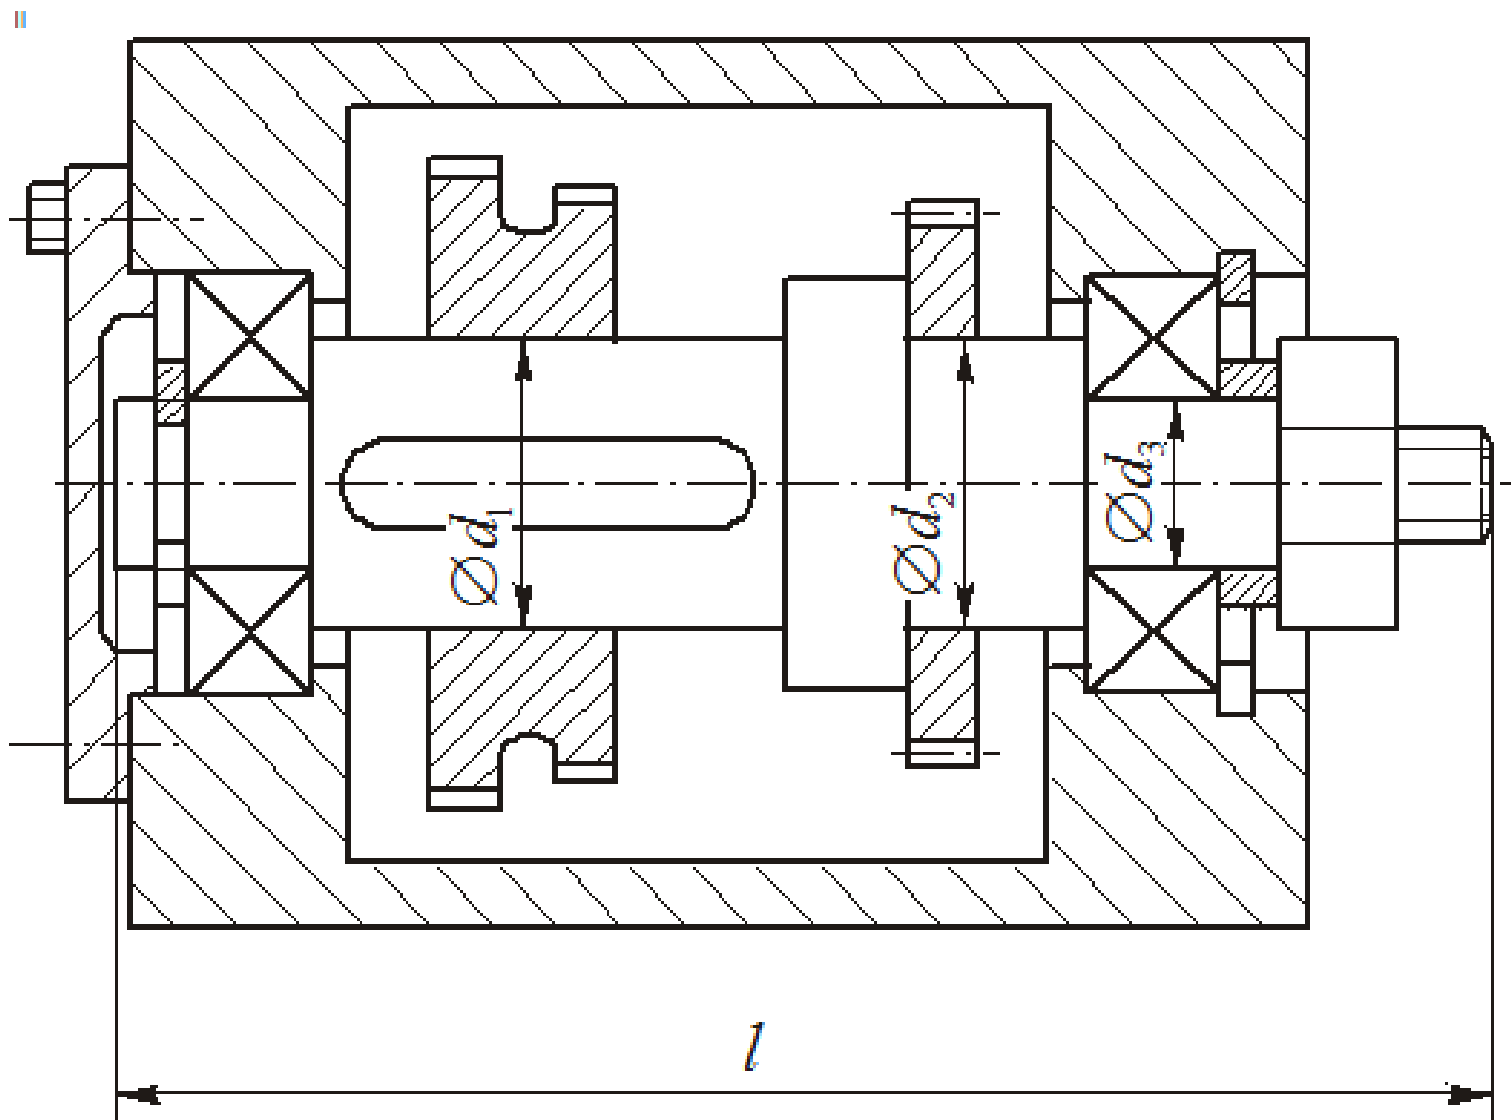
Пример сборочного эскиза редуктора без указания размеров и посадок (задание на ИДЗ-4)
